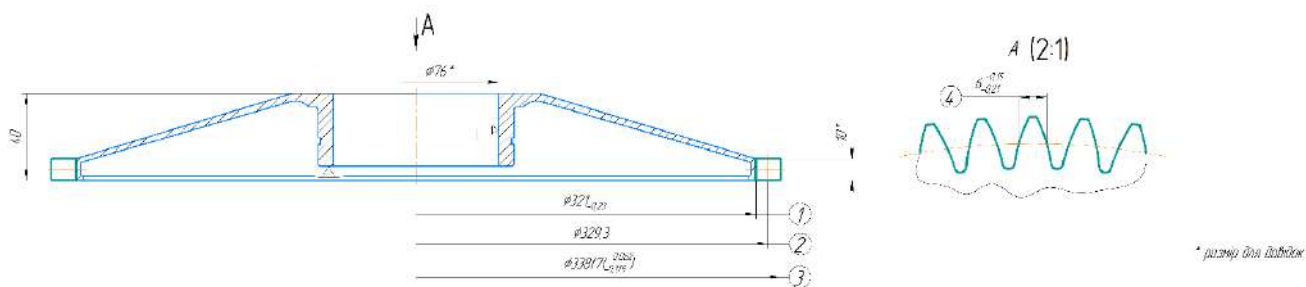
Експлуатаційний ескіз фрезерної операції
